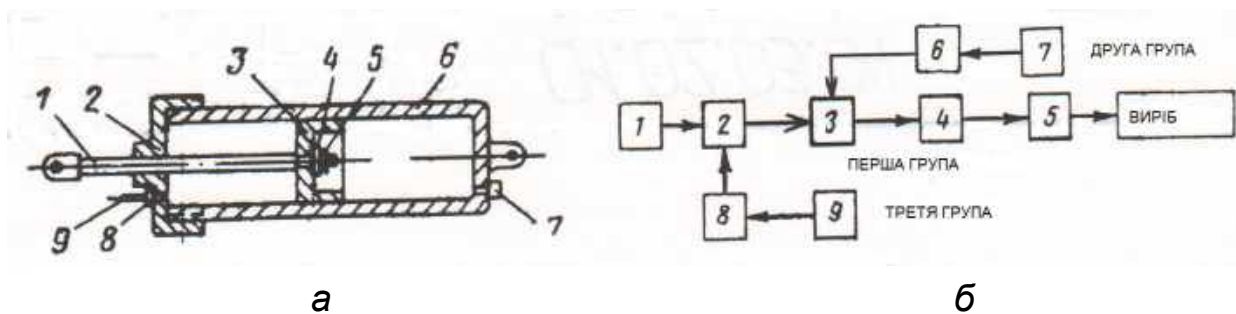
Силовий циліндр (а) і схема його складання за базовою деталлю (б): 1 – шток, 2 – кришка; 3 – поршень; 4 – шайба; 5 – гайка; 6 – циліндр; 7, 8 – штуцери; 9 – шланг
